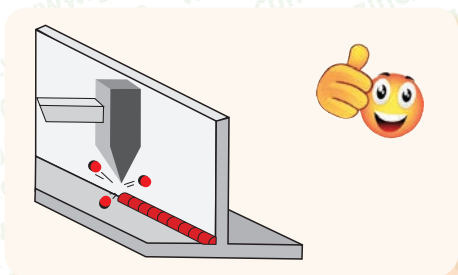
Élimination des résidus des flux de soudure par burinage et brossage métallique
